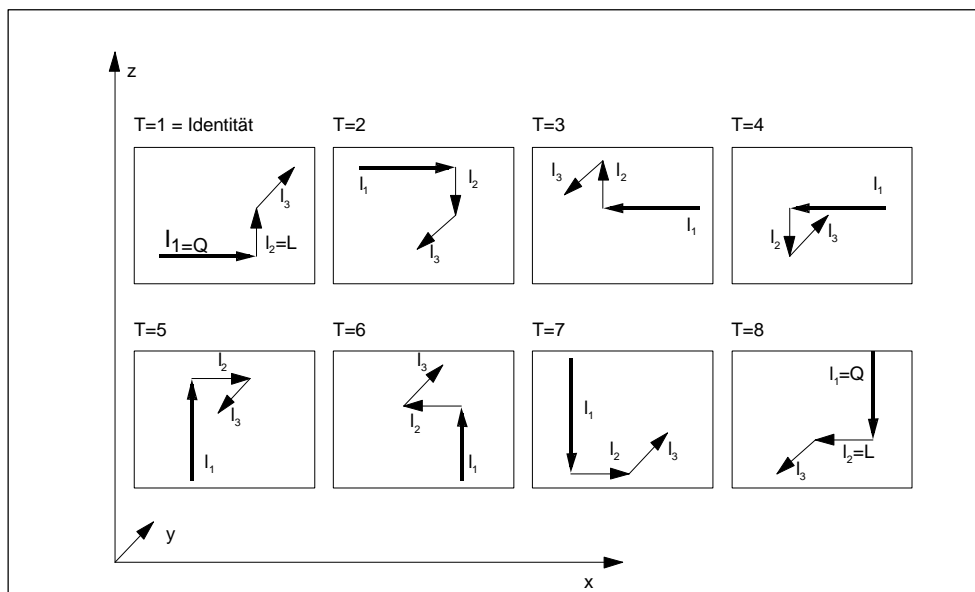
Die 8 definierten Transformationen (T = 1...8) für den Adapter mit G 18 und für ein Drehwerkzeug. Es werden die Zuordnungen der Werkzeuglängen I_1 , I_2 , I_3 auf die Geometrieachsen x, y, z gezeigt.
